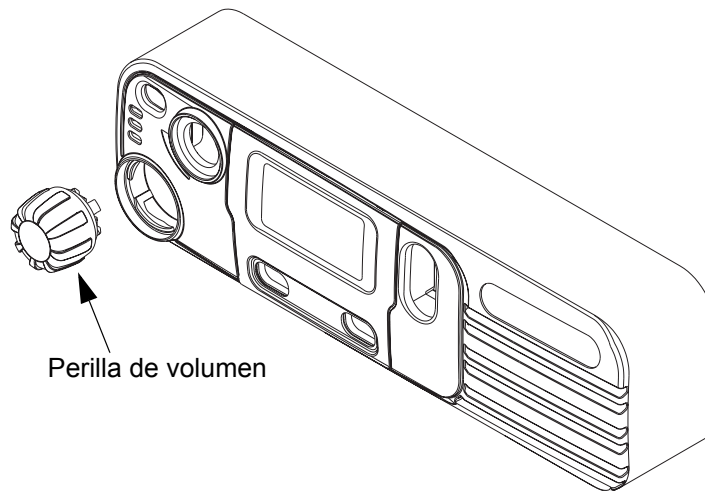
Desmontaje del parlante y de la perilla de volumen
